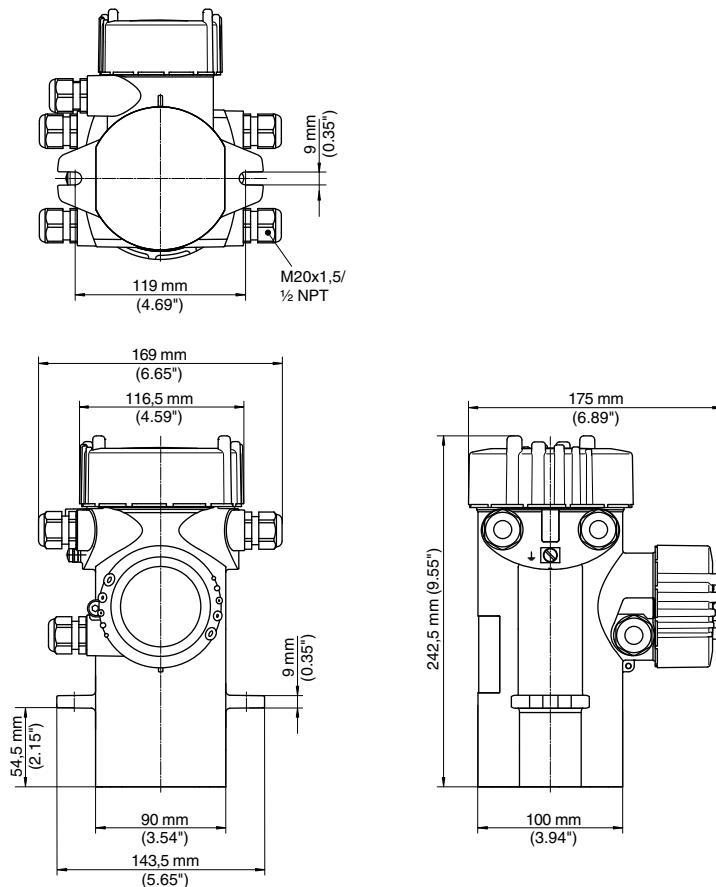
Корпус из алюминия или нержавеющей стали (точное литье)
